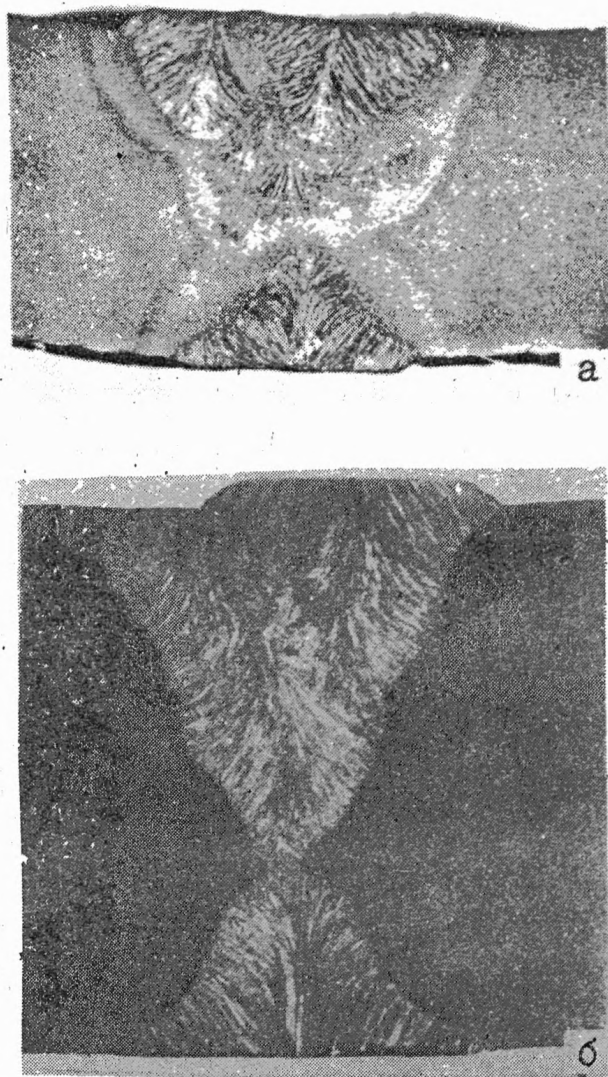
Многопроходная сварка стыкового соединения:
